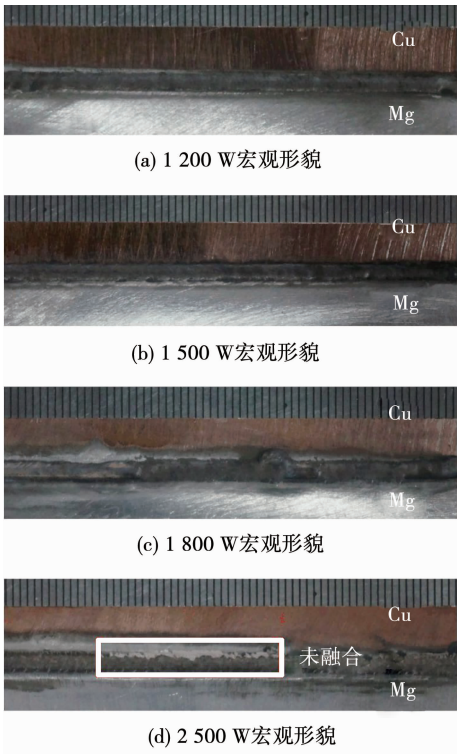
镁/铜激光填丝熔钎焊接头宏观形貌
